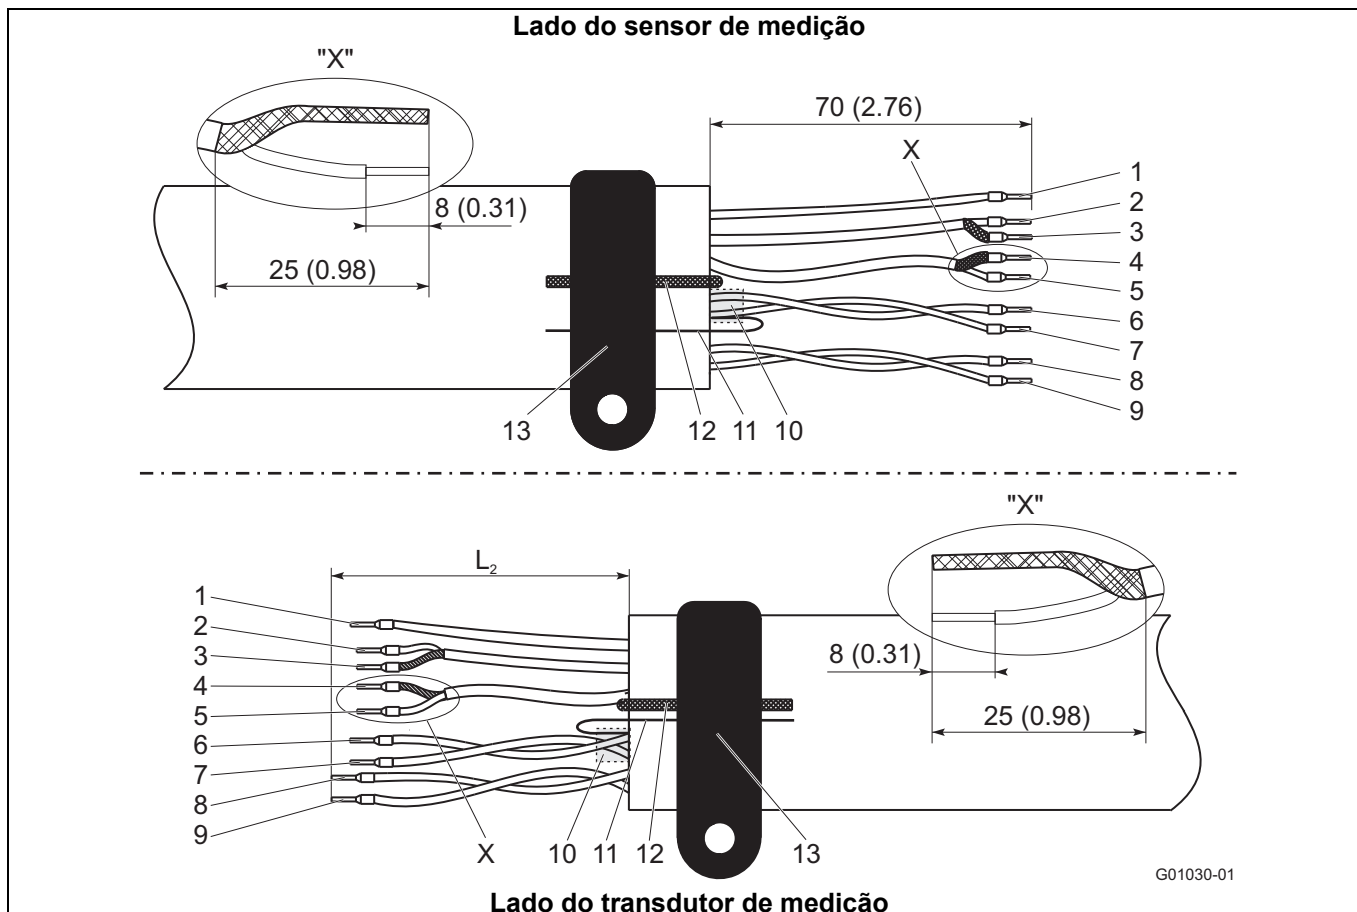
Lado do sensor de medição, dimensões em mm (inch)
